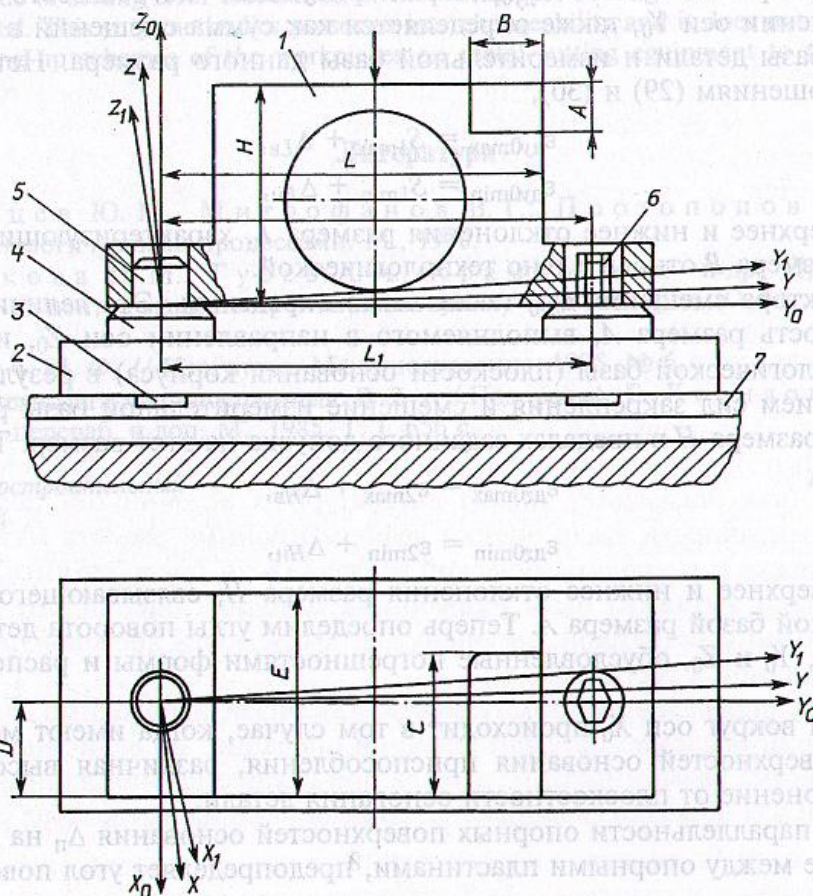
Схема для расчета погрешностей установки при базировании корпусной детали по плоскости и двум отверстиям: 1 — деталь; 2 — основание приспособления; 3 — направляющая шпонка; 4 — опорная пластина; 5 — палец цилиндрический; 6 — палец срезанный; 7 — стол станка
